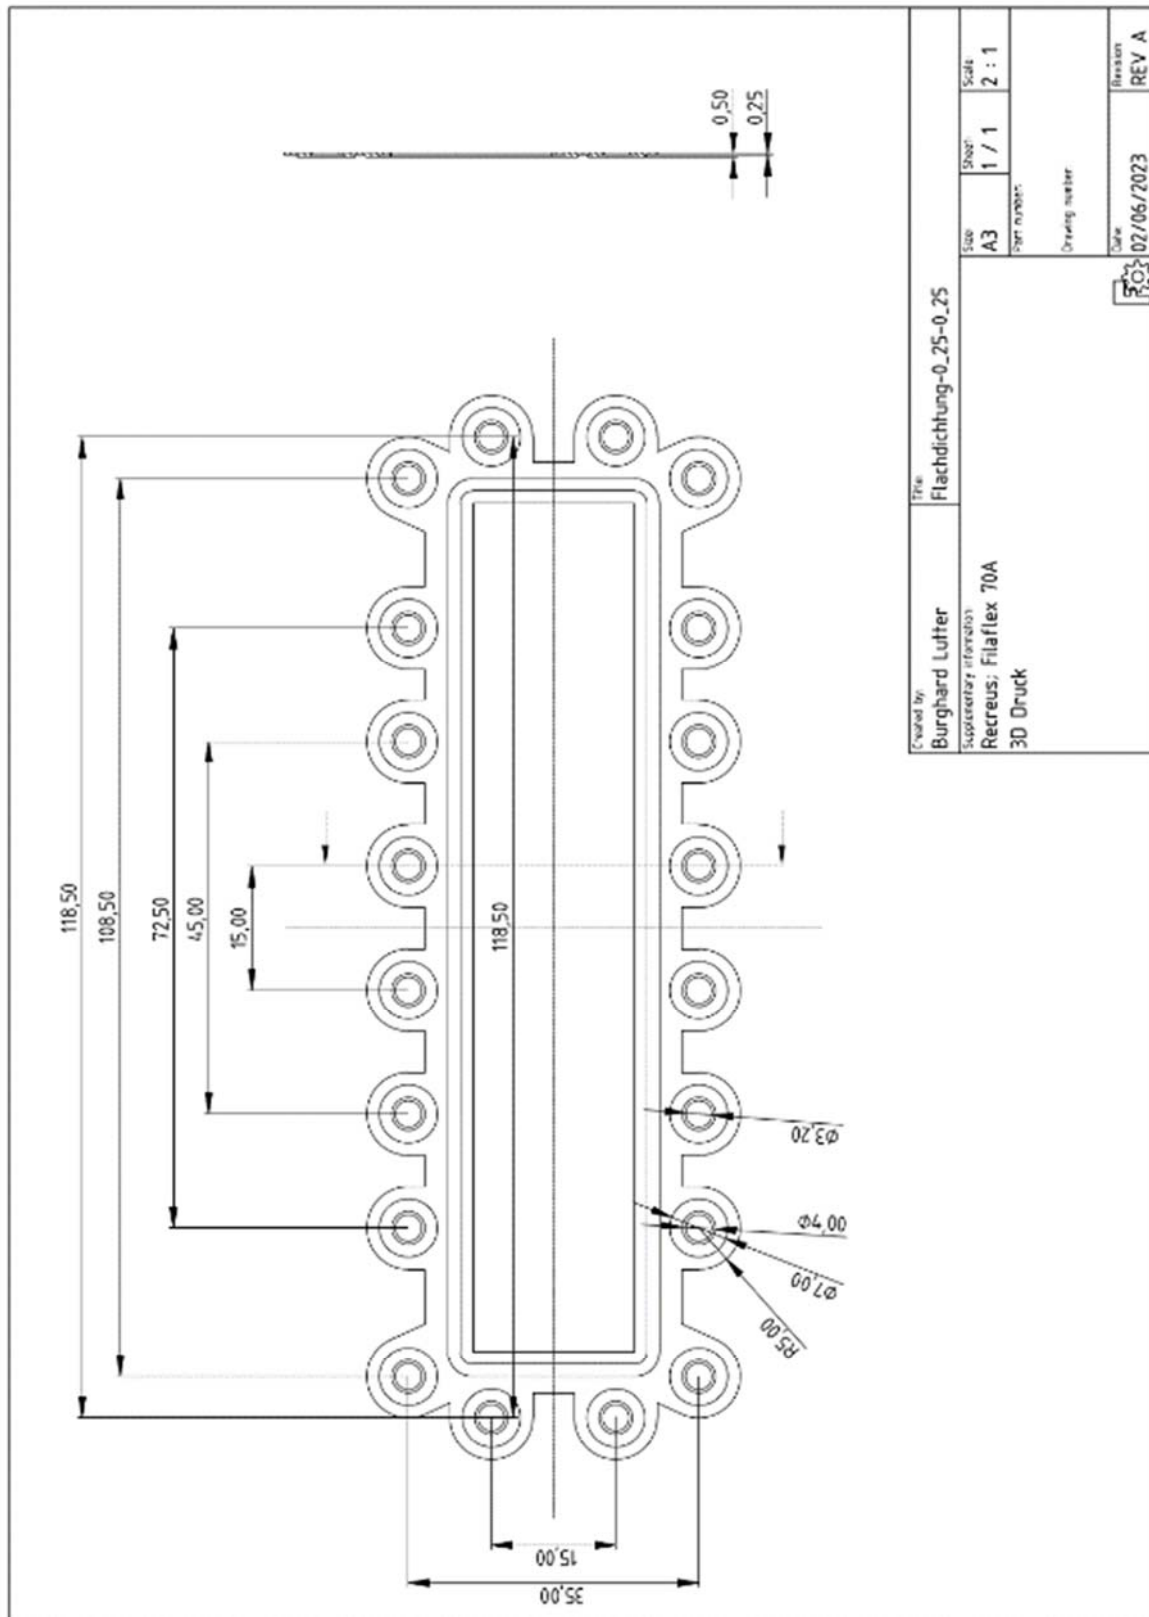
Technische Zeichnung der Flachdichtung
